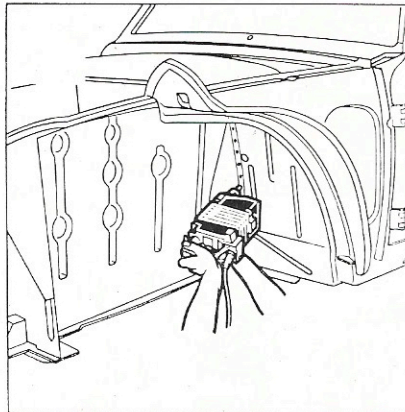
Soudage de la doublure avant gauche sur tablier (double point DP 38 ARO).
